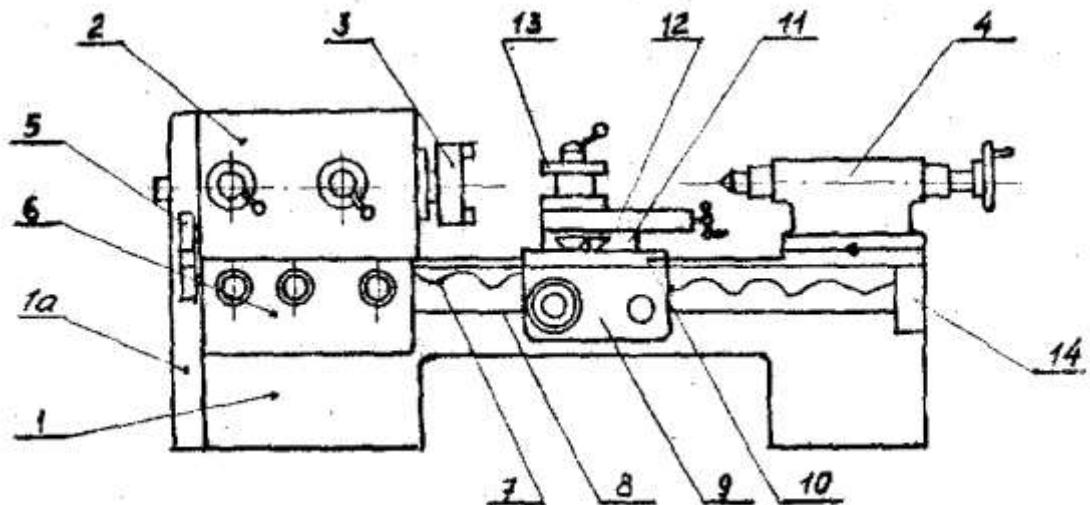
I. Універсальний токарно-гвинторізальний верстат
